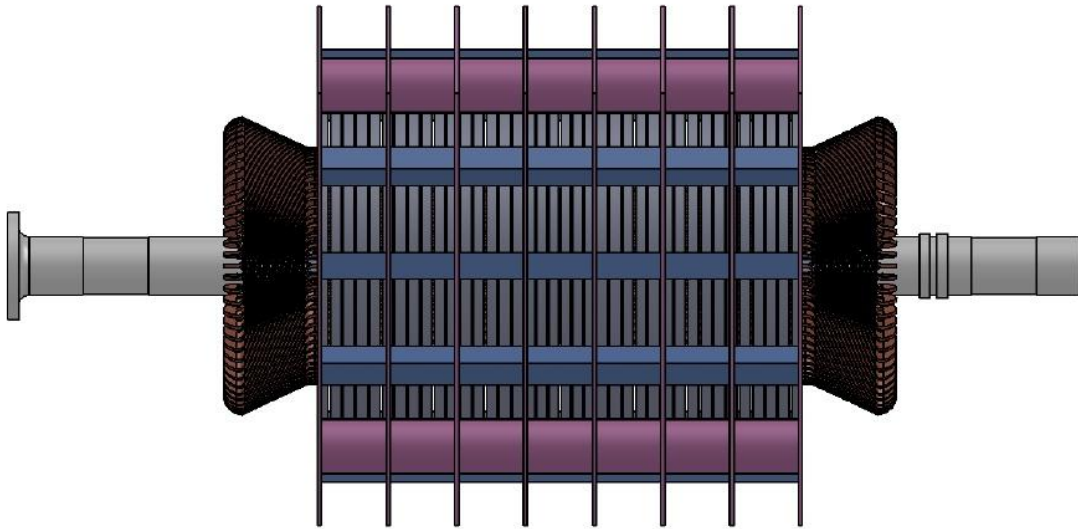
Navinutý rotor, vinutí zajištěno drážkovými klíny
